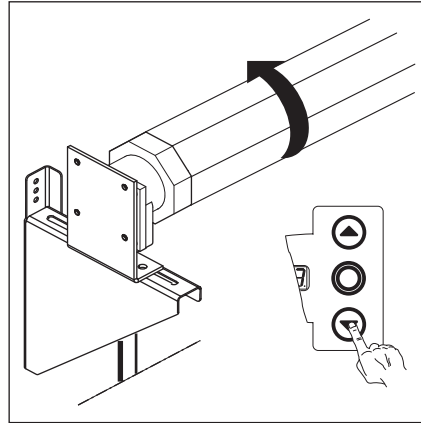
Движение наматывающего вала в направлении *Ворота Закр.*, пока конечный выключатель не отключит двигатель
